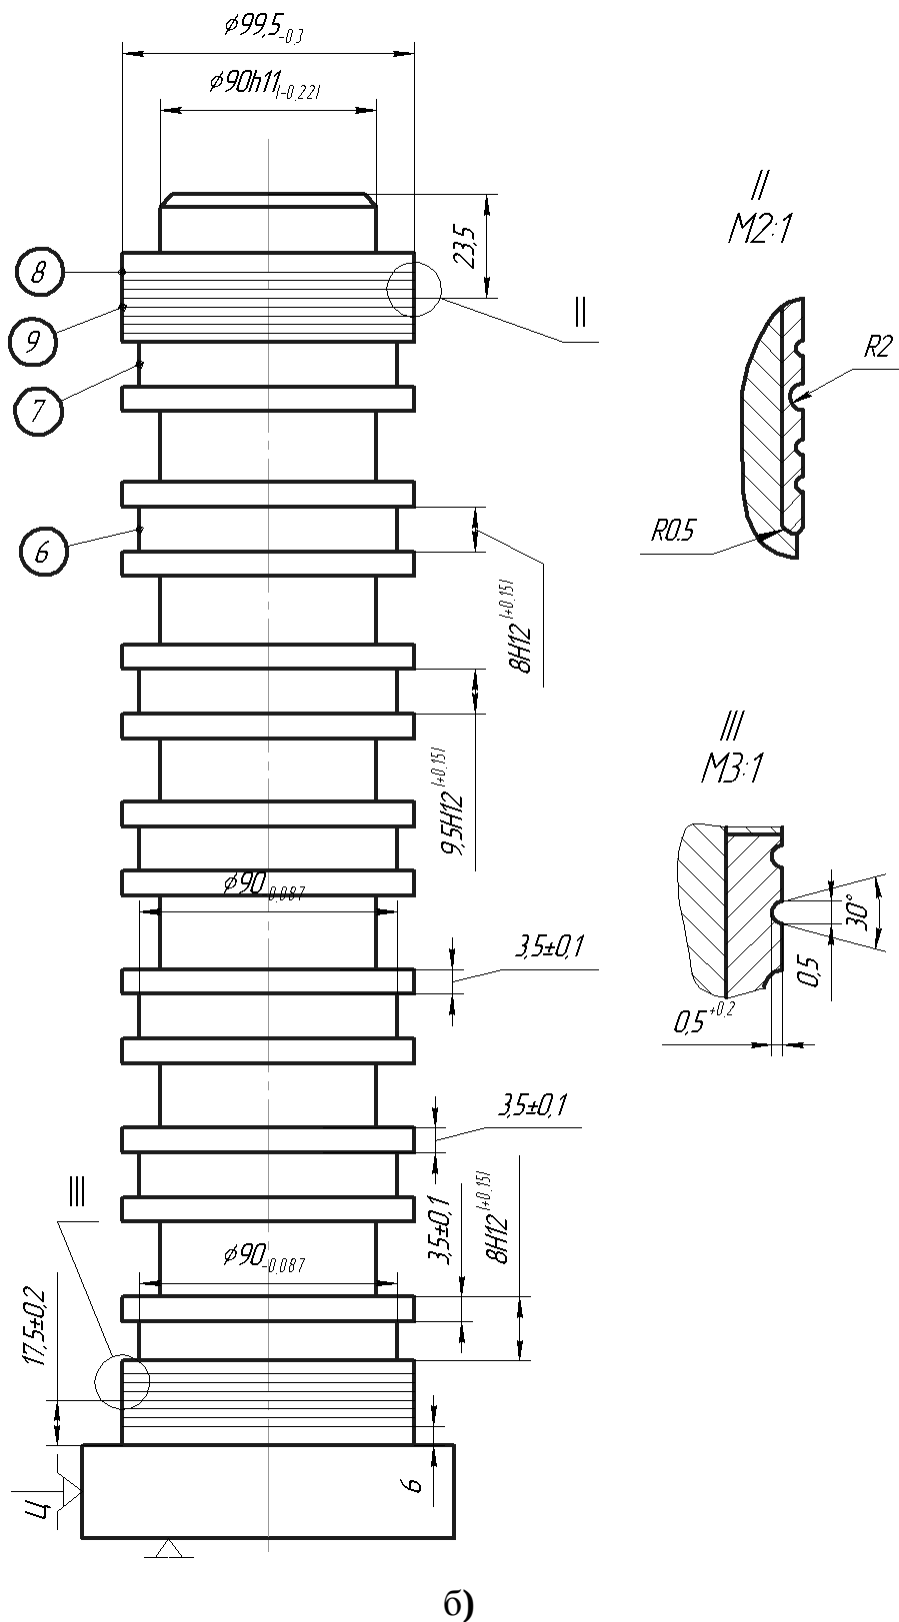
Схема базування і обробки деталі на операції 025
